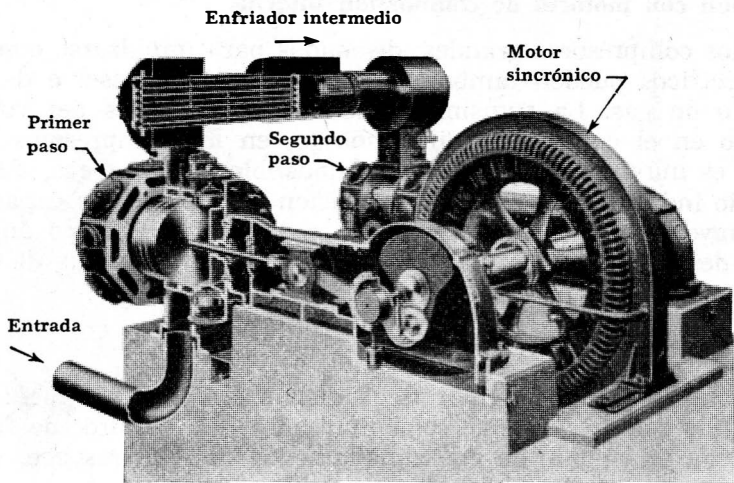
Compresor de dos pasos impulsado por motor sincrónico. (Cortesía de Ingersoll-Rand Company.)
